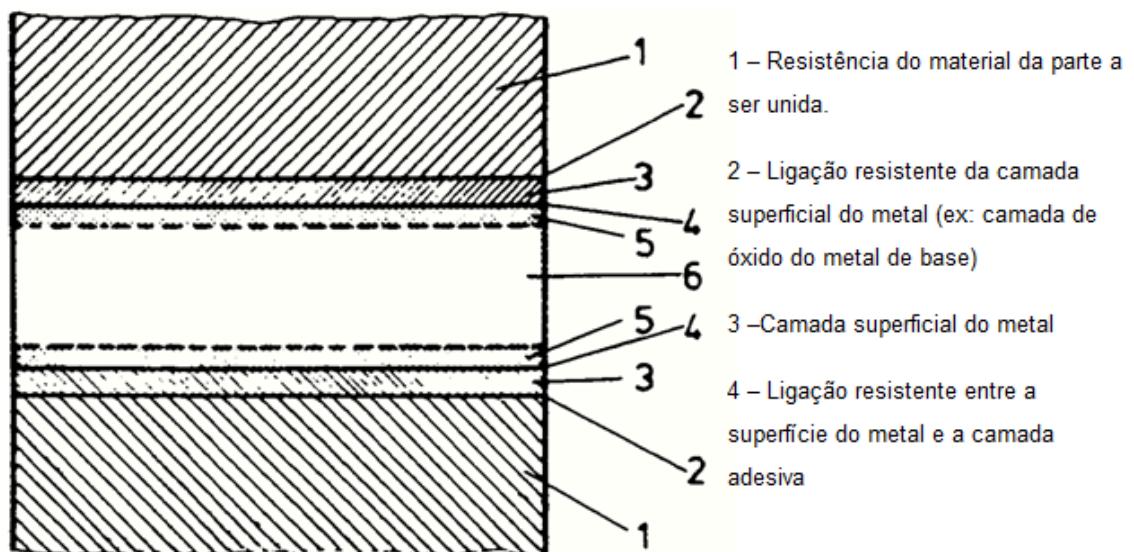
Configuração de uma junta soldada por adesão
